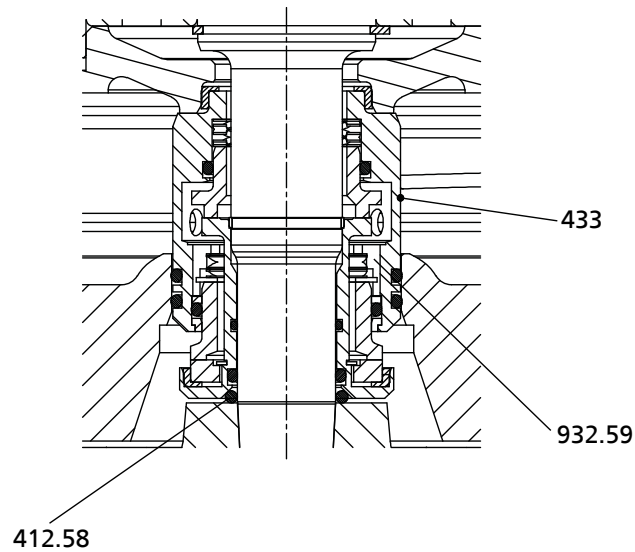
Einbauplan Doppelgleitringdichtung in Cartridge-Ausführung
